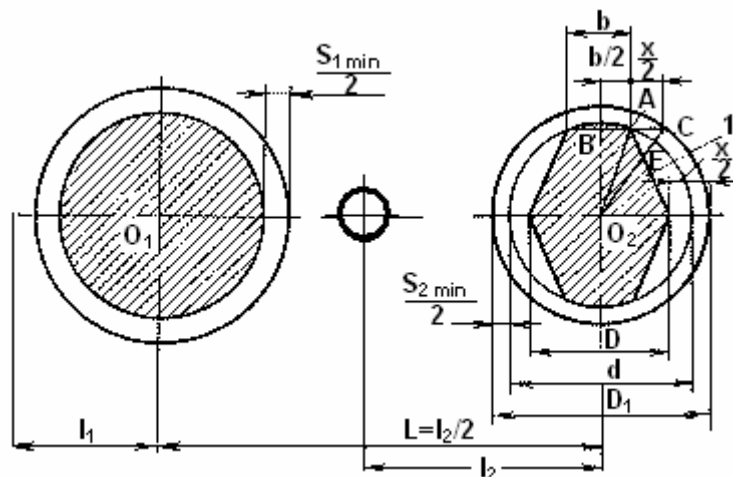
Схема для визначення похибки базування при установленні корпусної деталі на два пальці
